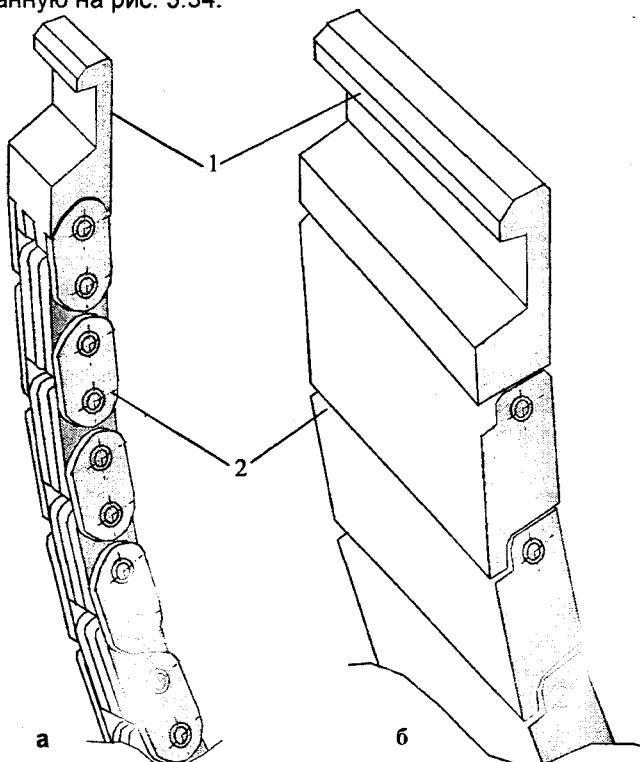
Схемы гибких затравок с нераздвижными (а) и раздвижными (б) звенями: 1 – головка; 2 – тело
